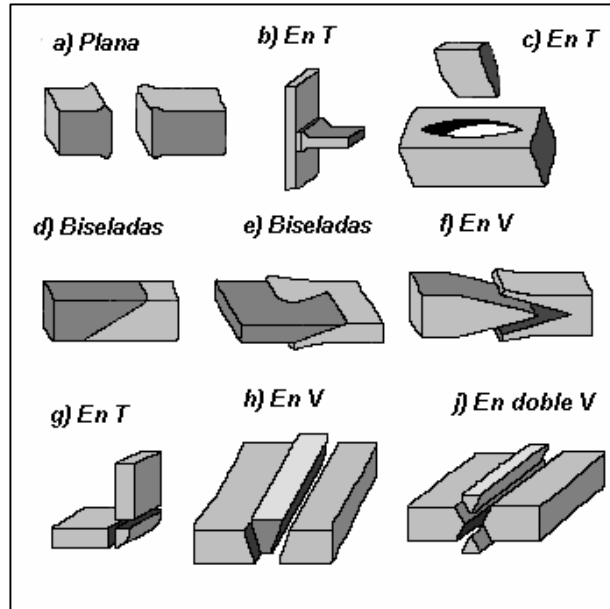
Diseño de juntas, utilizado en procesos de soldadura al fuego.
